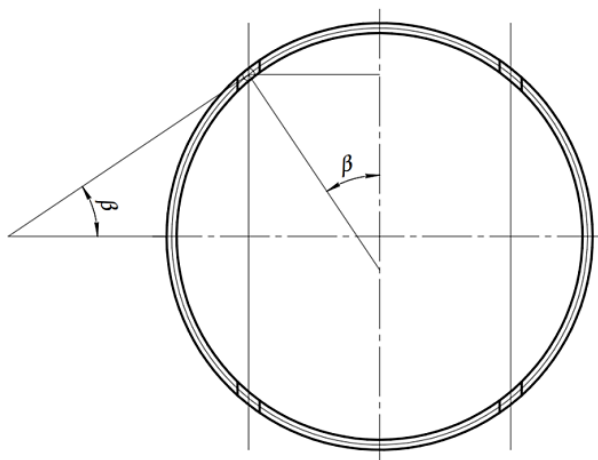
Поперечное сечение трубы рамы [Cross section of frame tube]
